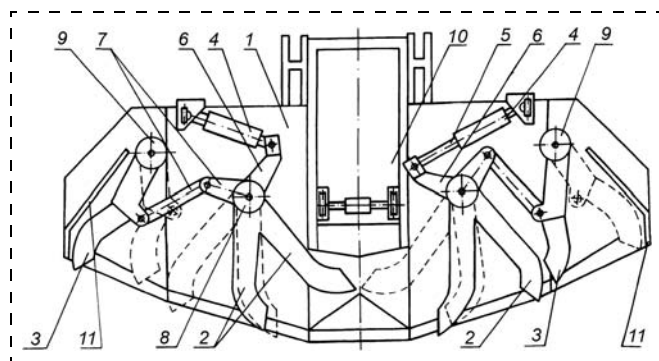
Многогребковый погрузочный орган со встречным движением основных и периферийных гребков: 1 — наклонный питатель; 2 — основной гребок; 3 — периферийный гребок; 4 — гидроцилиндр; 5 — шток гидроцилиндра; 6 — рычаг; 7 — система рычагов; 8, 9 — опоры; 10 — конвейер
